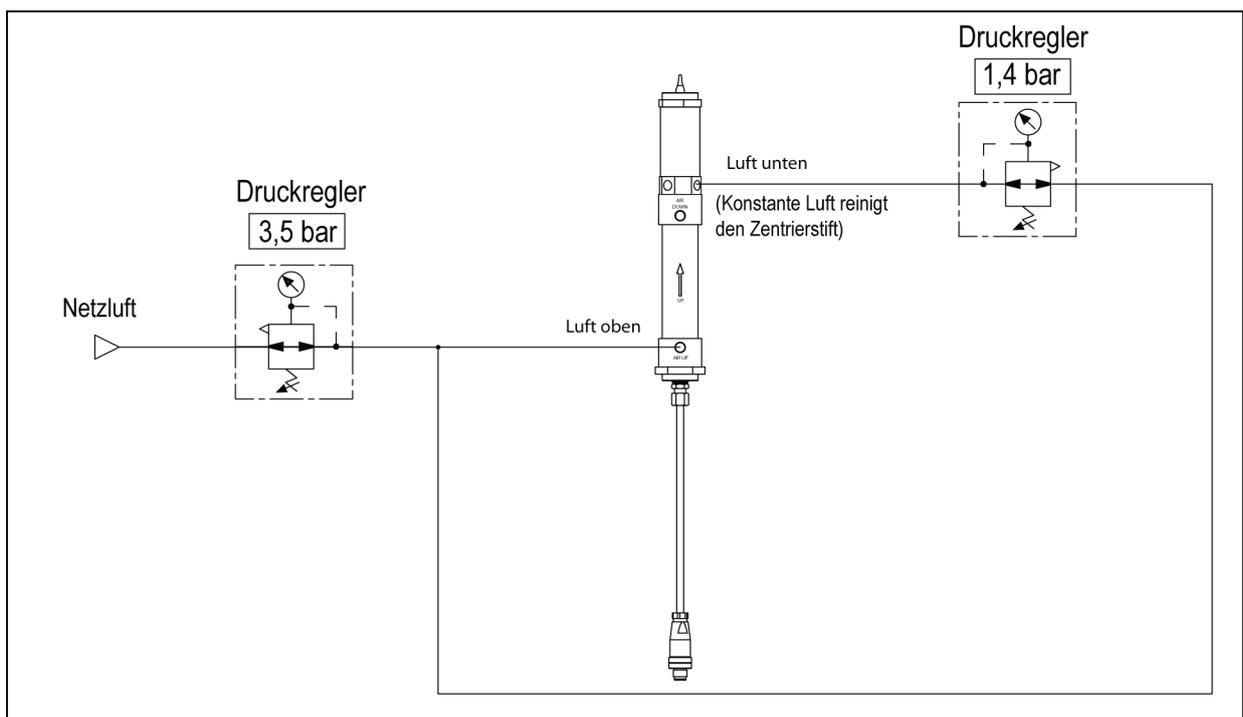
Pneumatik Anschlussplan nur für geklemmten LVDT-Schweisskörper mit nicht-rückziebarem Zentrierstift.
